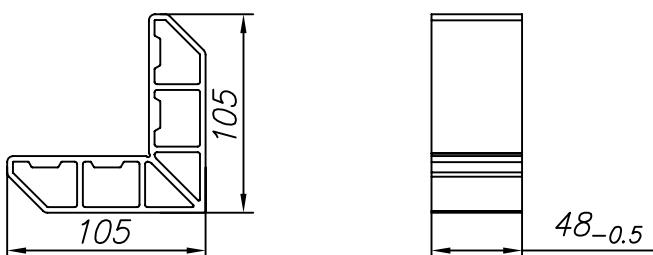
Изготовление соединителя углового FLGU.400.0910
